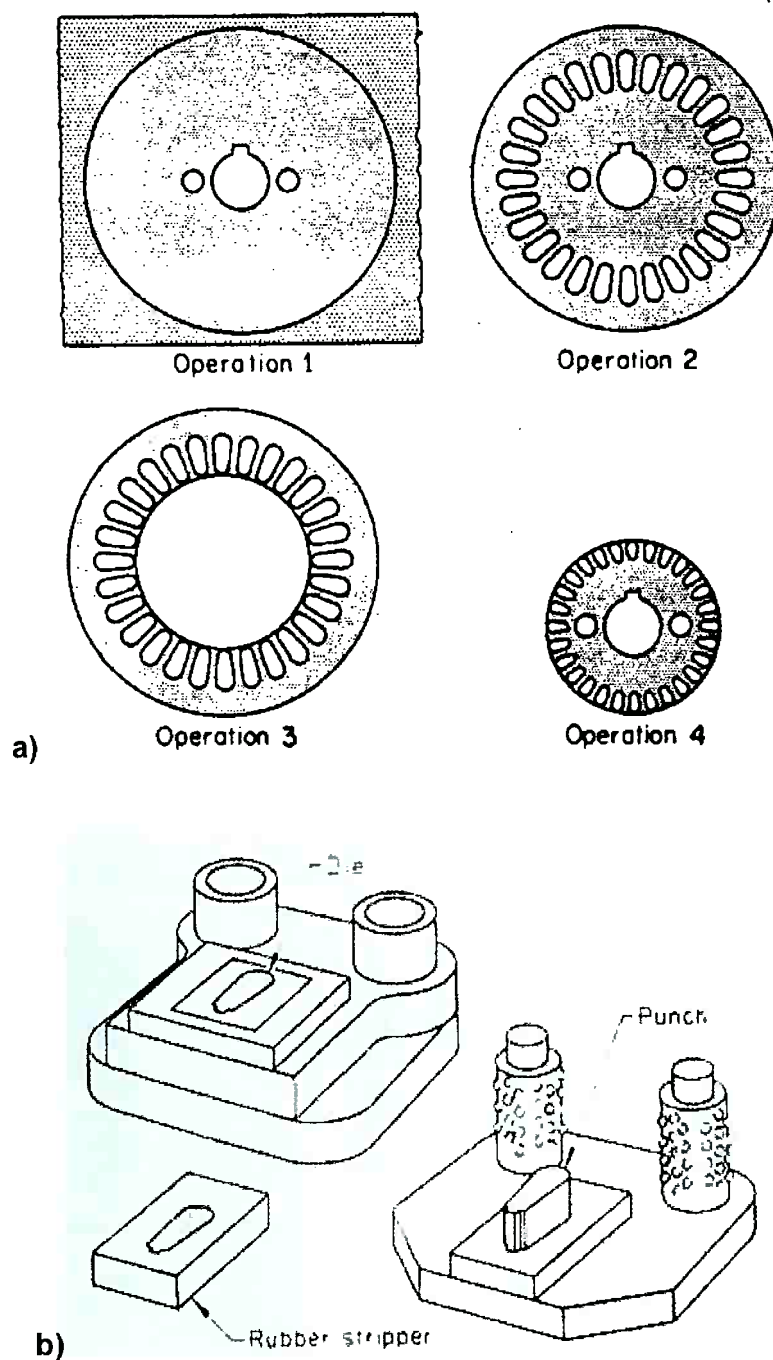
Produtos e ferramentas de produção em operações únicas. a) Rotor e estator produzidos em operações únicas; b) Ferramentas de entalhe único.
